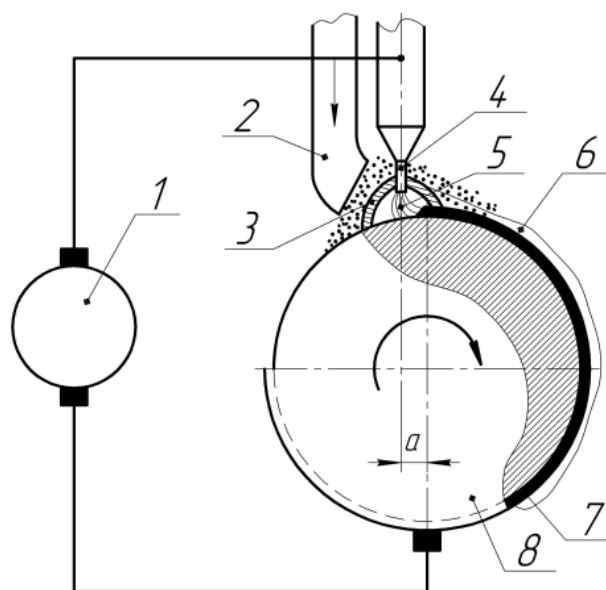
Схема автоматичного наплавлення деталі під шаром флюсу:
